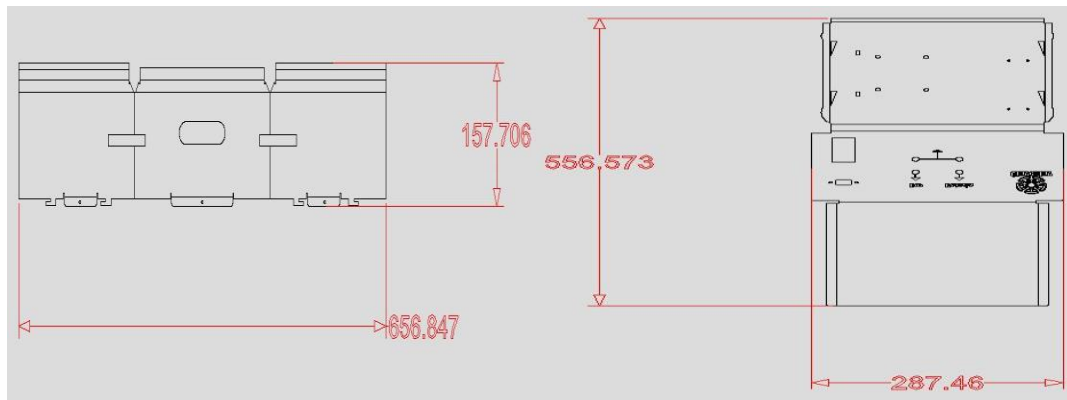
Planos de corte de la estructura Di Pr.
